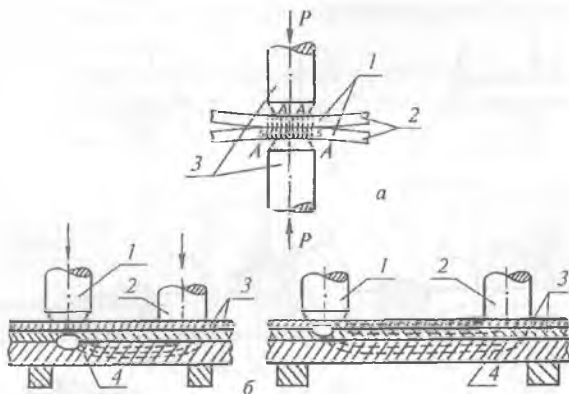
Схема точечной сварки: а — двухсторонняя: 1 — линия тока; 2 — свариваемые детали; 3 — медные стержни-электроды; А-А — площадки контакта электрод-деталь; Б-Б — площадки контакта деталь-деталь; б — односторонняя: 1 — сварочный электрод; 2 — токопроводящий электрод; 3 — свариваемые детали; 4 — вспомогательная токопроводящая подкладка
